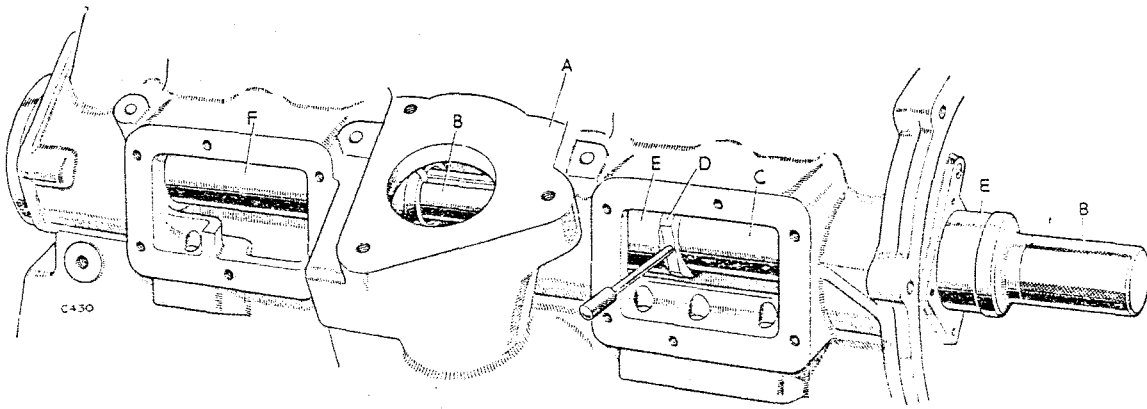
Montaje de los cojinetes delanteros del árbol de levas.
